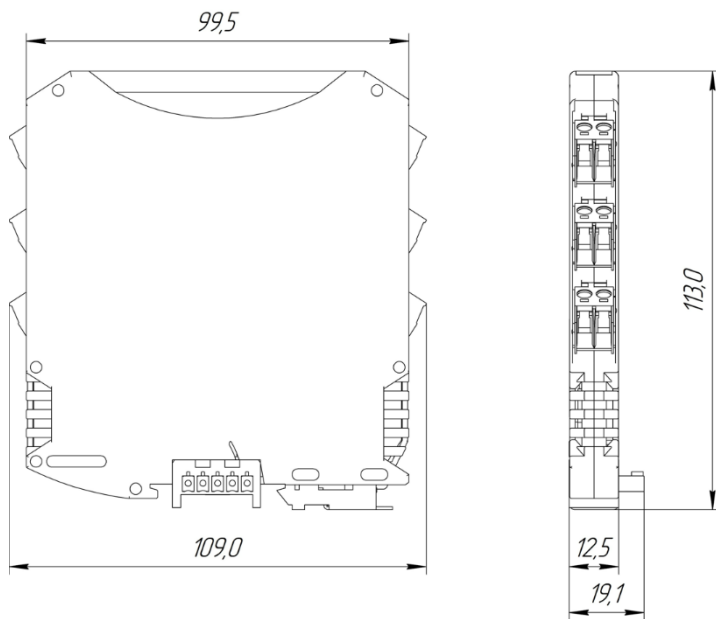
Габаритный чертеж преобразователя в узком корпусе
